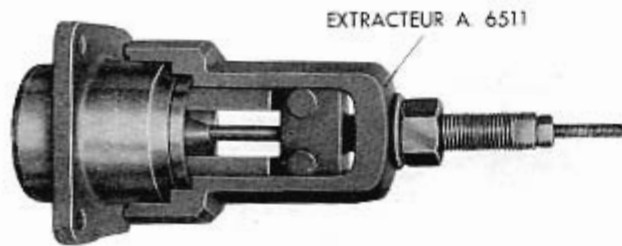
Extraction de la bague extérieure du roulement extérieur du moyeu de roue arrière.
